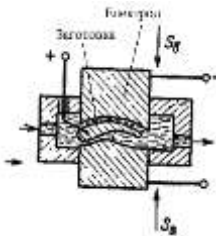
Електрогідравлічна розмірна обробка
